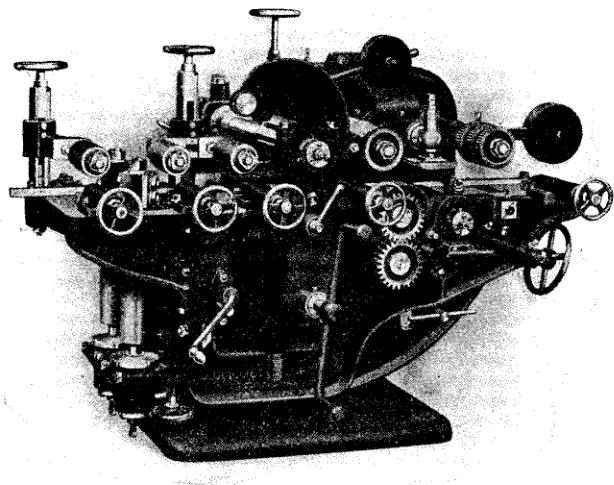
Machine à raboter, à bouveter et à faire les moulures.
